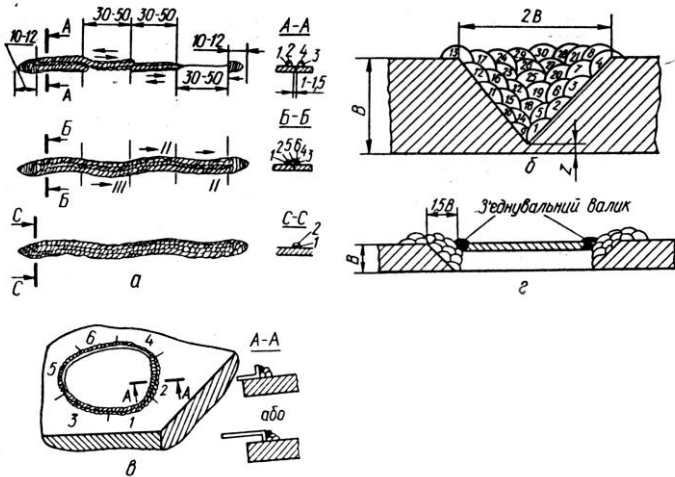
Схема накладання швів при зварюванні чавунних корпусних деталей: а – тріщин у тонкостінних деталях без наступної механічної обробки; б – тріщин у товстостінних деталях з наступною механічною обробкою; в – підготовка пробойн і порядок зварювання при накладанні латки внапуск; г – вварювання вставки у пробійну деталі
